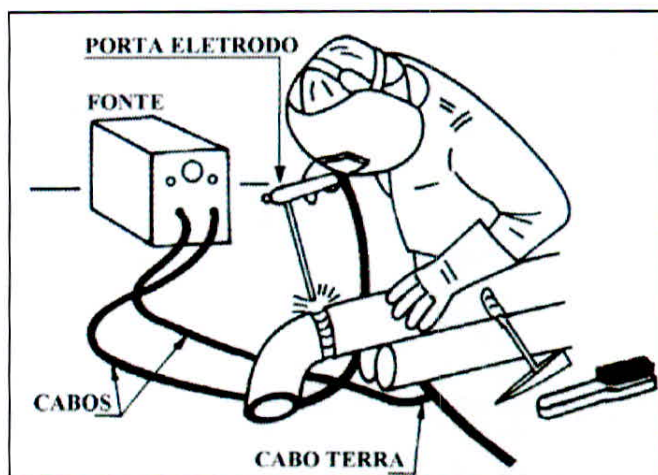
Esquema de equipamentos de soldagem com eletrodos revestidos.
